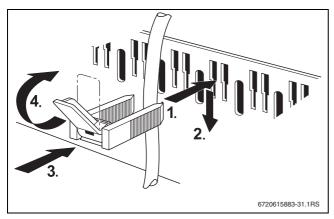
Fissaggio dei cavi mediante fascette serracavo
